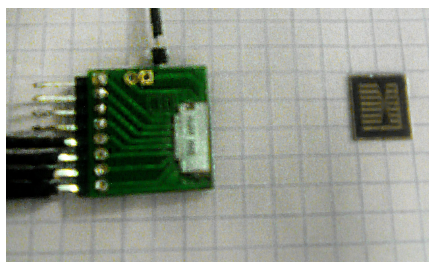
Support micro-SD soudé sur un PCB relié à des câbles, à côté d'une puce
